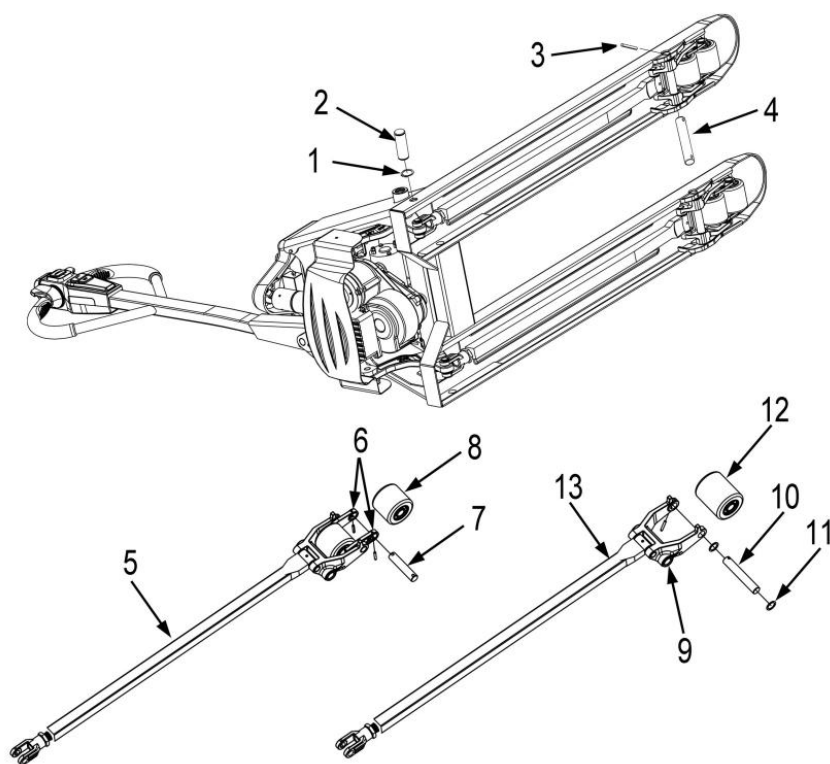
Vista explodida do conjunto de rolos de carga.
